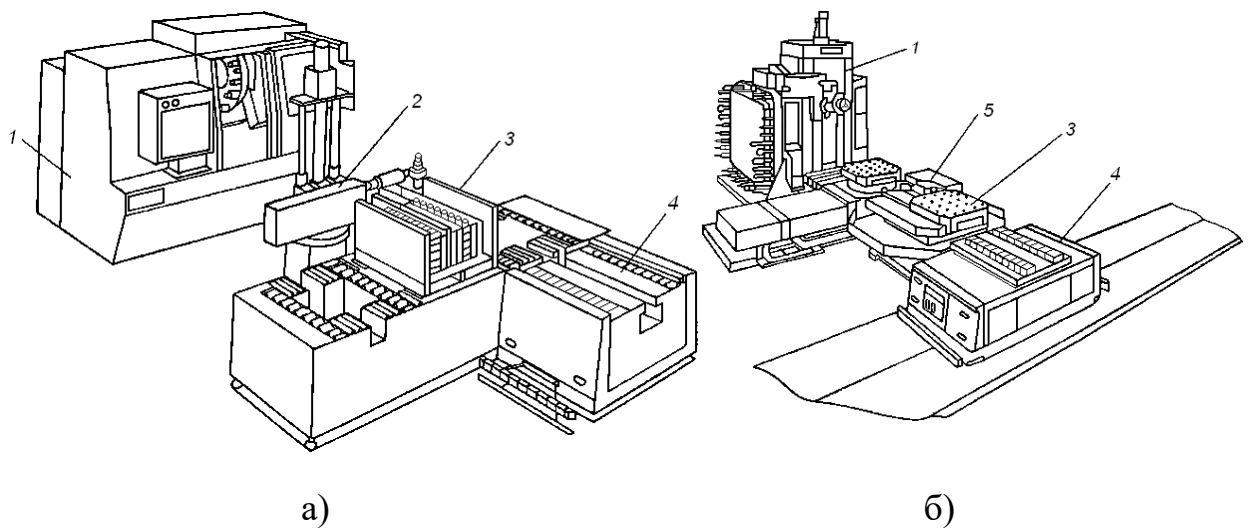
Загальні види РТК для обробки деталей типу «тіла обертання» (а) і корпусних деталей (б): 1 – обробний центр; 2 – обслуговуючий робот; 3 – операційний накопичувачі; 4 – транспортний робот; 5 – завантажувальний пристрій
